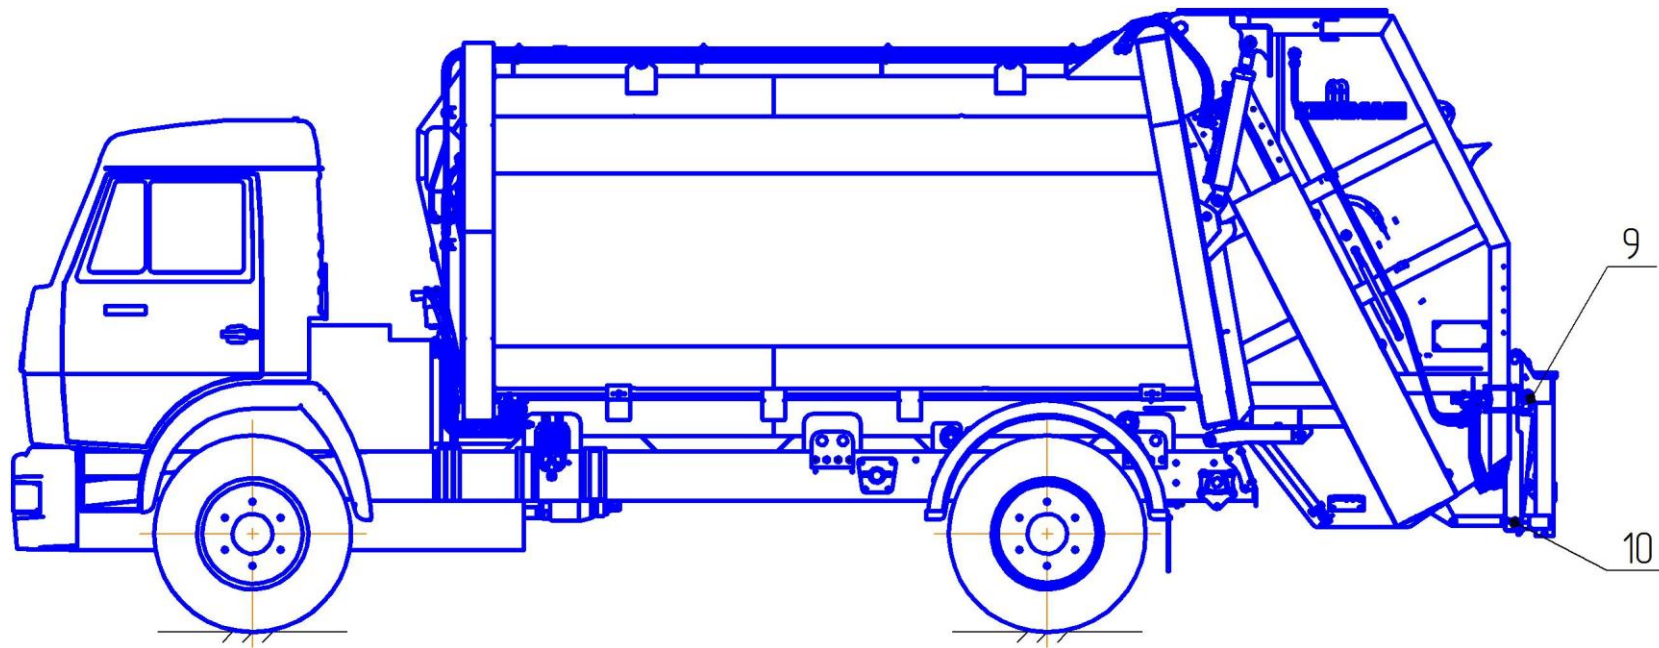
Схема смазки мусоровоза без опрокидывателя
